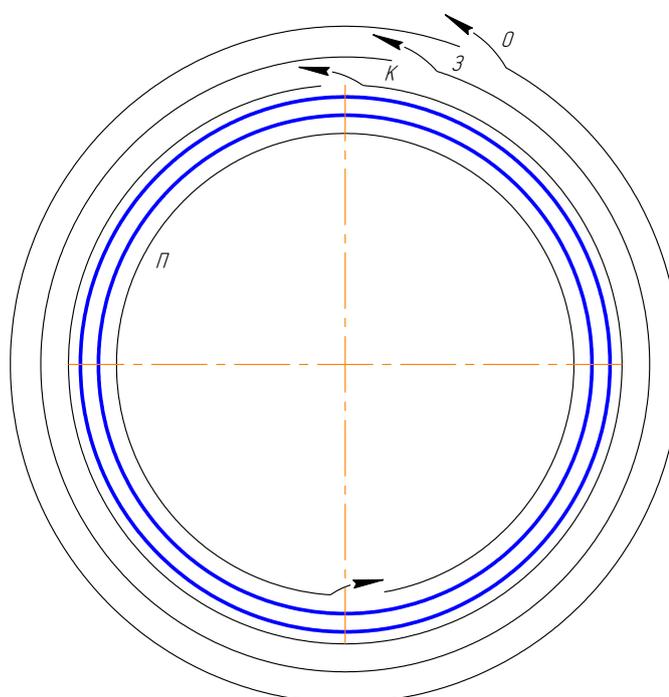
Схема двухсторонней автоматической сварки под слоем флюса
